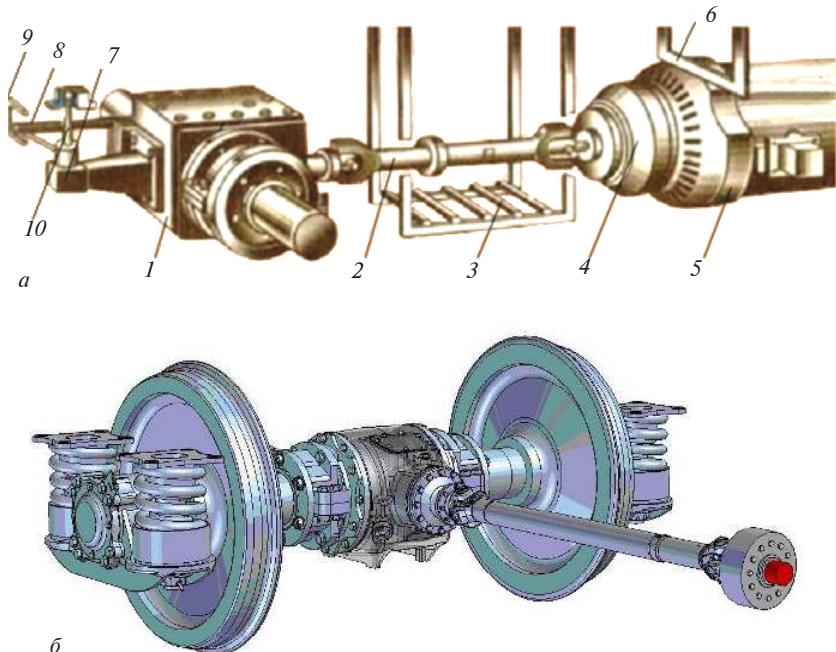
Редуктор EUK-160-1M (а), редуктор WBA-32/2 (б):
